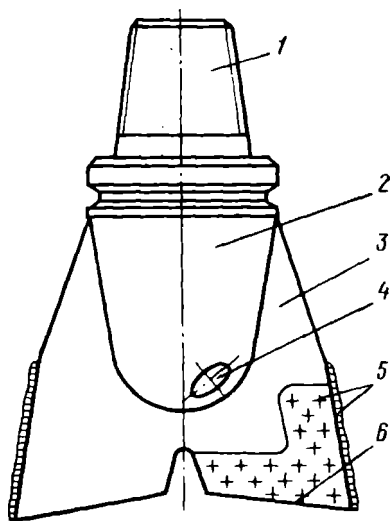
Долото лопастное («рыбий хвост»): 1 — головка с соединительной резьбой; 2 — корпус; 3 — лопасть; 4 — промывочное отверстие; 5 — покрытие твердосплавное; 6 — режущая кромка
